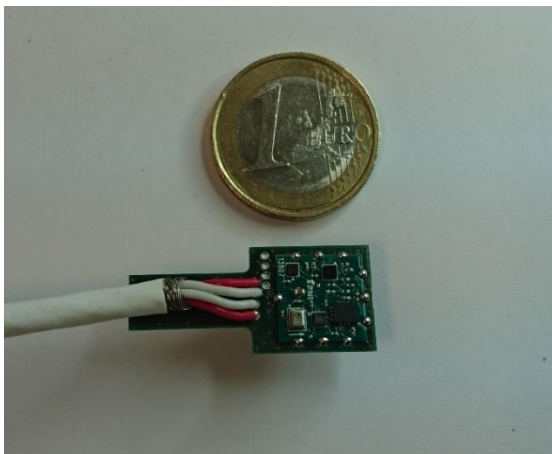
Prototypelektronik des Verlaufssensor nach der kompletten Bestückung
